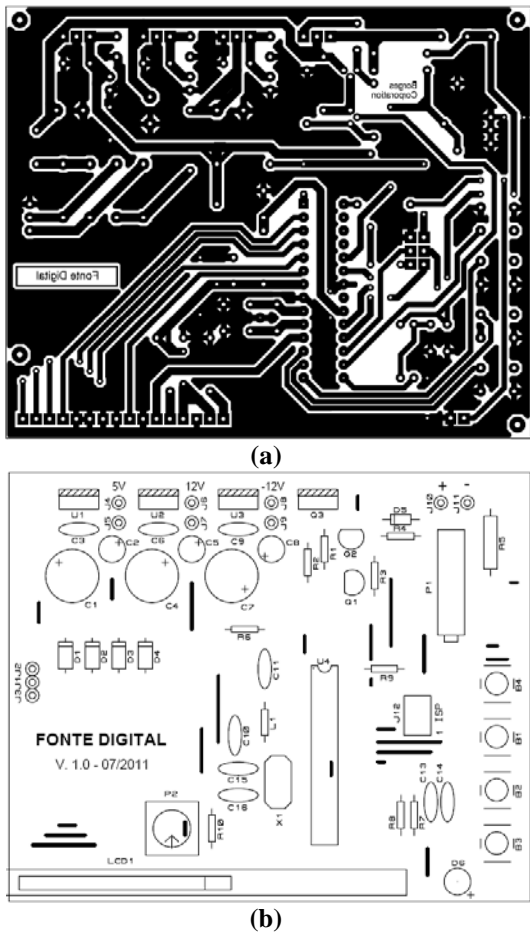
Layout da PCI, com (a) bottom layer e (b) top silk.
